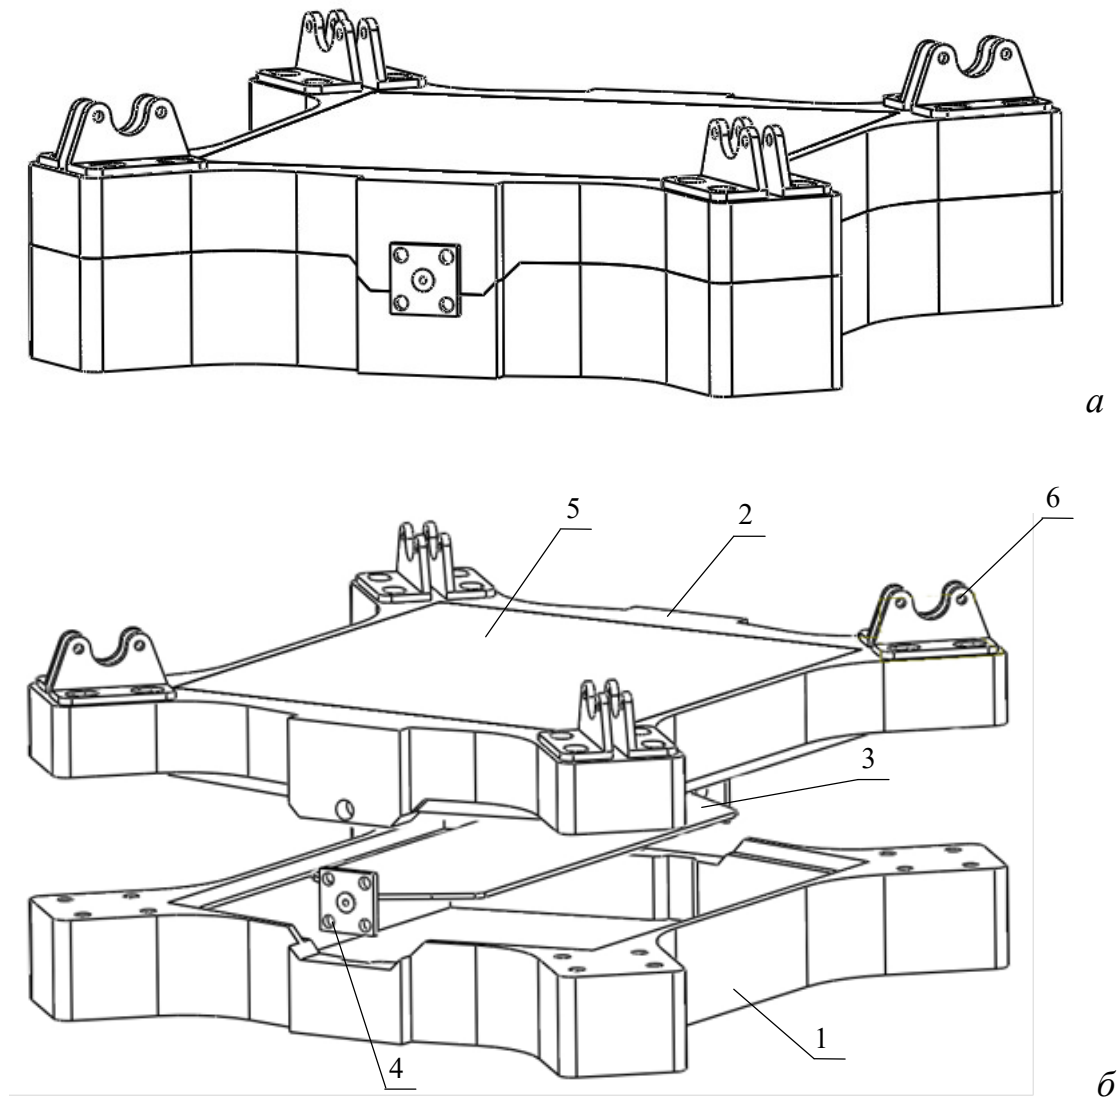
Изометрический вид (а) и компоненты конструкции (б) твердотельной модели ТЕМ камеры: 1 – основание корпуса, 2 – крышка, 3 – центральный проводник, 4 – СВЧ-соединители, 5 – испытательный стол, 6 – зажим
